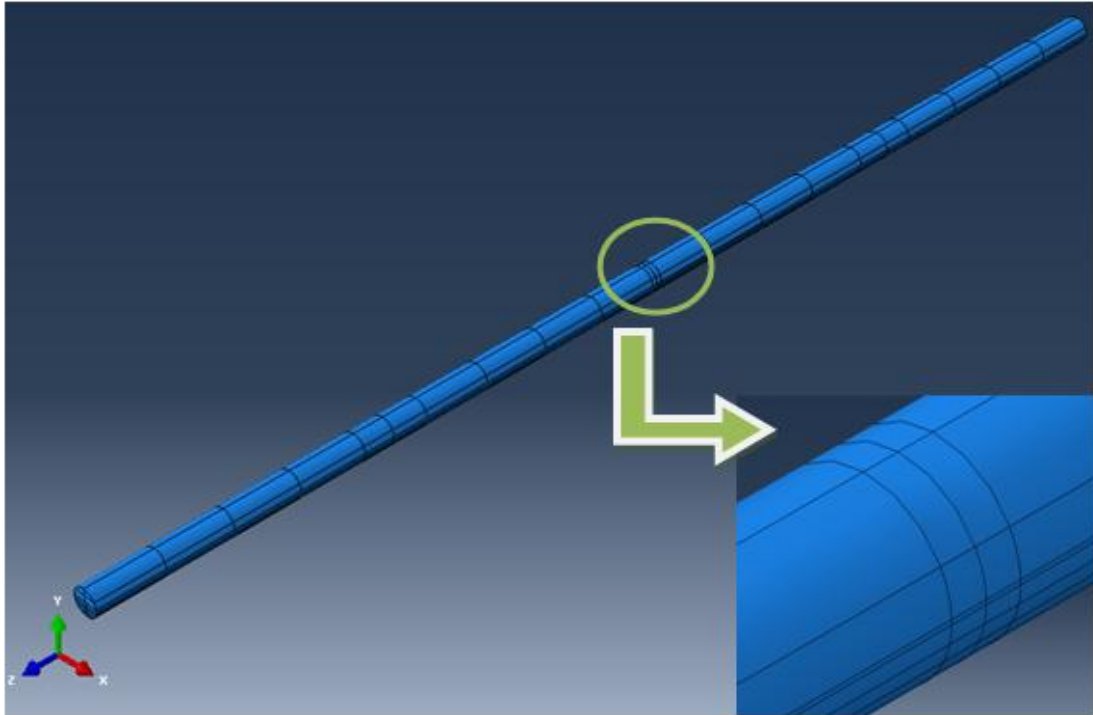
4.- Detalle de la partición en la sección de la fisura.
